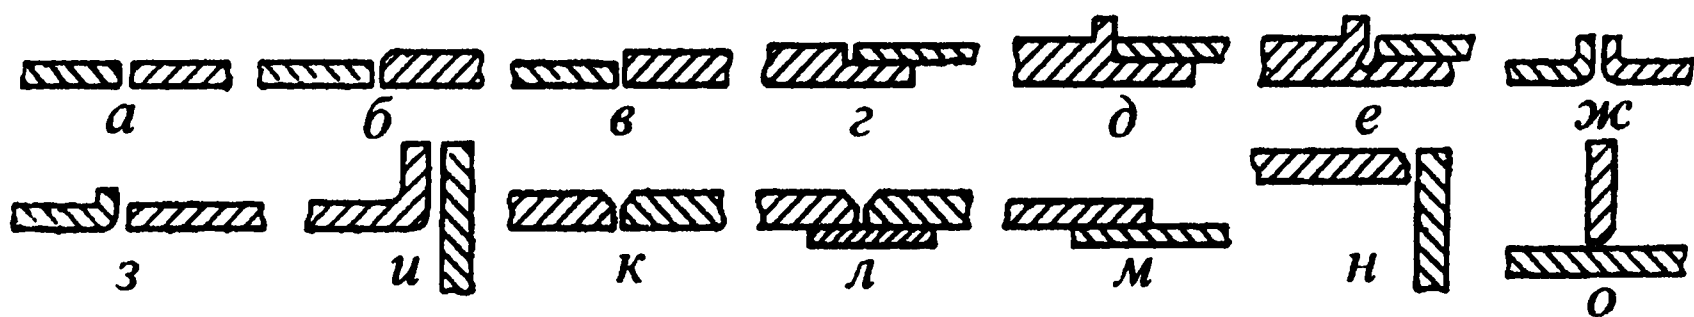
Виды соединения для аргонодуговой сварки:
